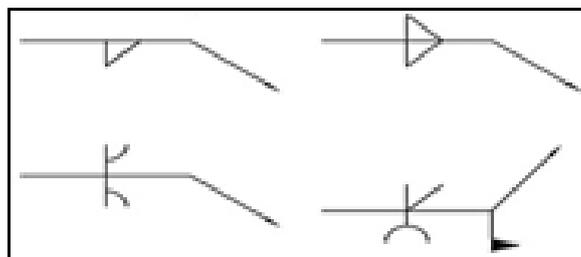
Indicación de simetría asimetría de la soldadura.
